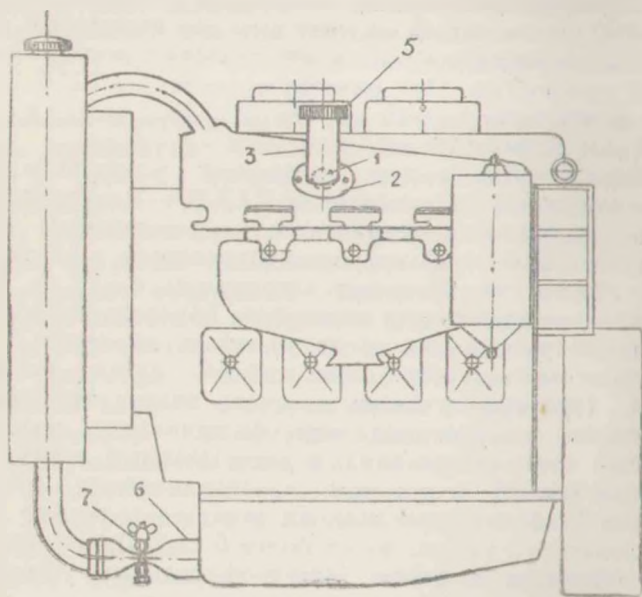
Схема устройства приспособления для интенсивного разогрева двигателя ЯАЗ-204 водой.
